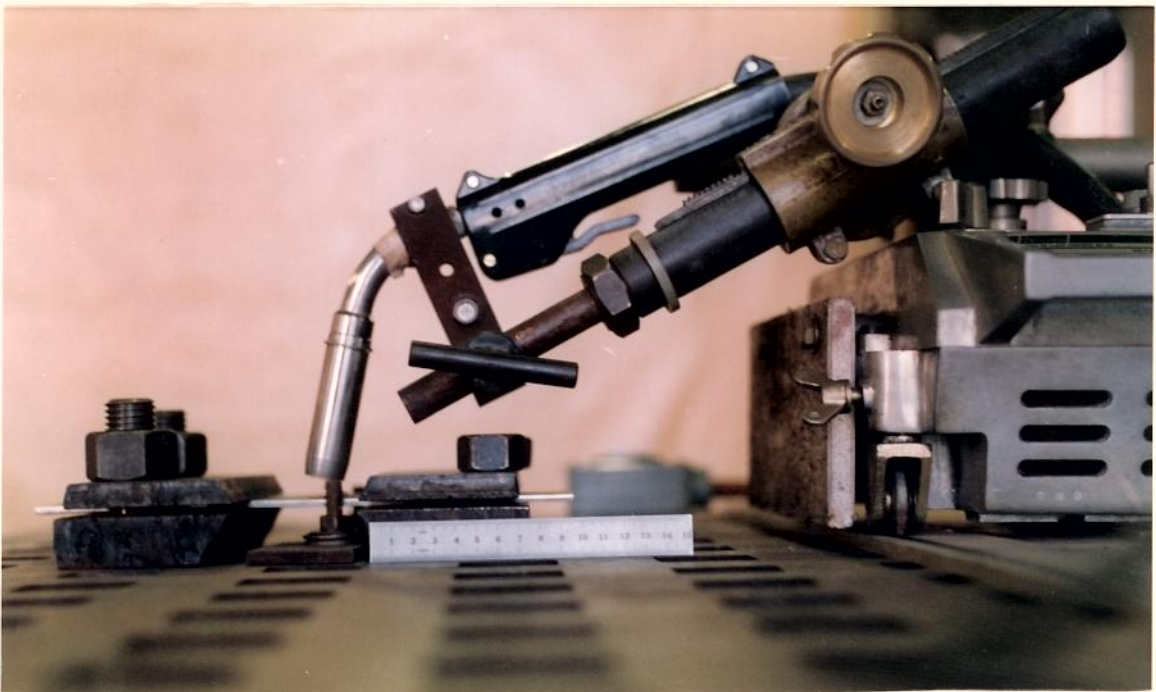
Dispositivo de fixação das chapas e da tocha de soldagem.
